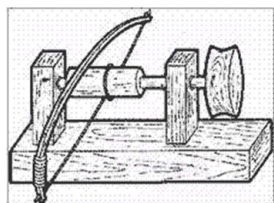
Перший відомий пристрій для обертання заготовок
